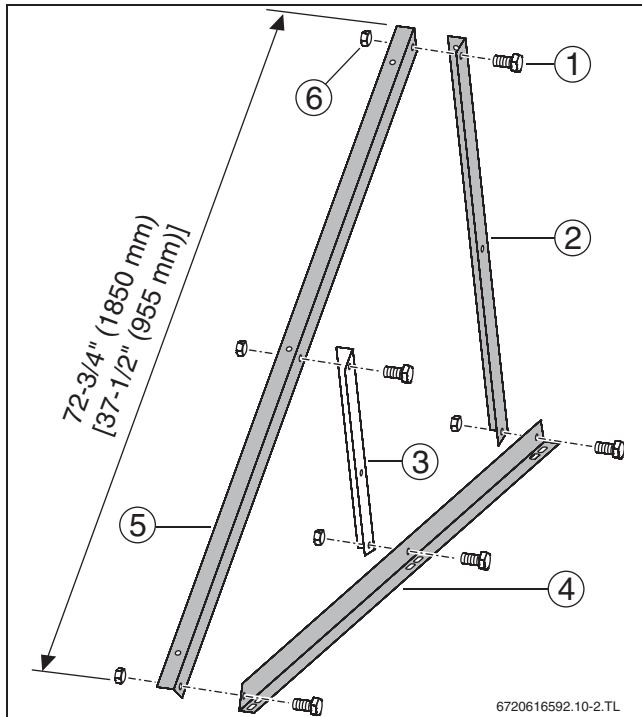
Соедините стойки винтами и гайками (размеры в скобках = для горизонтального расположения коллекторов)
